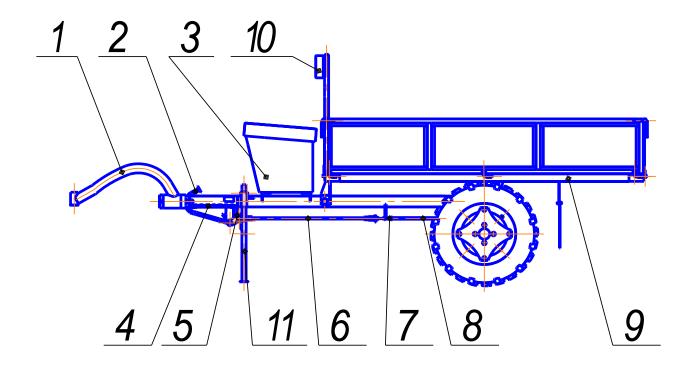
Прицеп мотоблочный ПМ 1 – кронштейн поворотный; 2 – рычаг тормоза; 3 – сиденье; 4 – балка; 5 – винт; 6 – натяжитель; 7 – регулировочный винт; 8 – трос; 9 – рама; 10 – спинка; 11 – подставка
